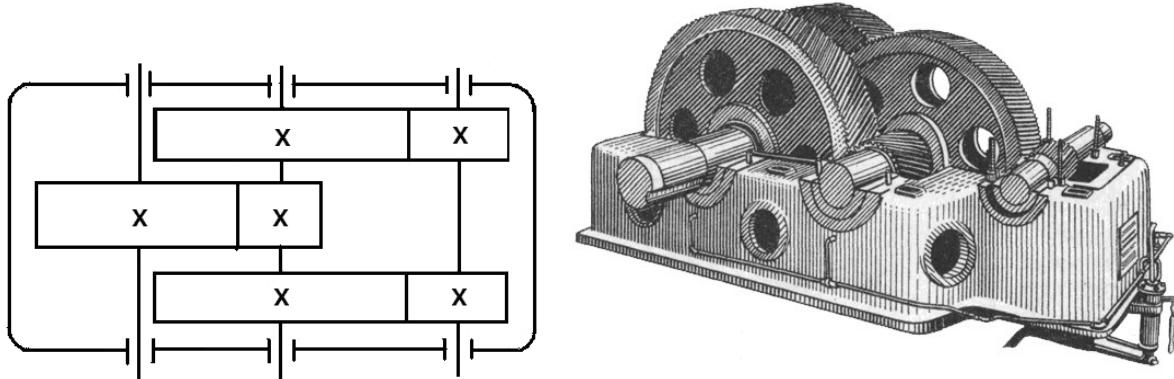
Цилиндрический двухступенчатый редуктор: с раздвоенной тихоходной ступенью, схема и вид – с раздвоенной быстроходной ступенью
